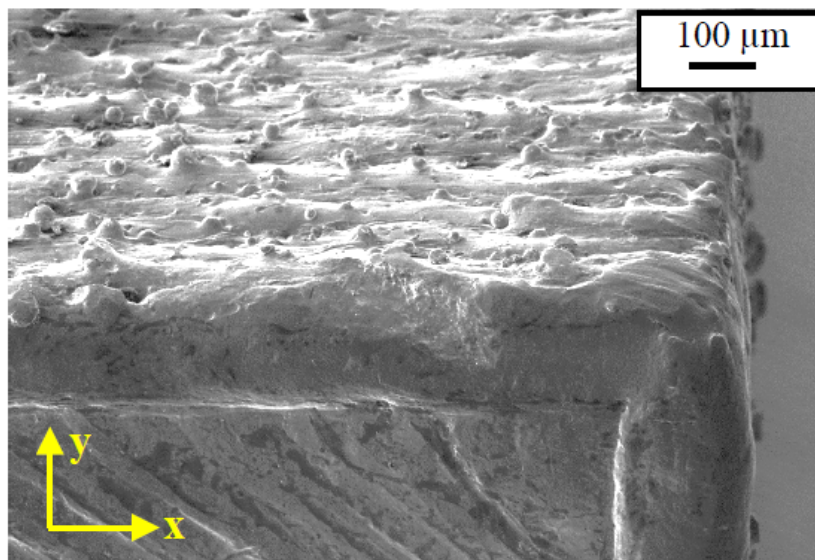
Superfície de Inconel 718 fabricado pro manufatura aditiva após a soldagem (Sadiq et al. (2018)).
